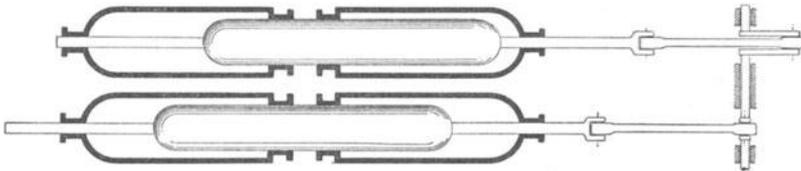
Druckpumpe mit vierfacher Wirkung.
